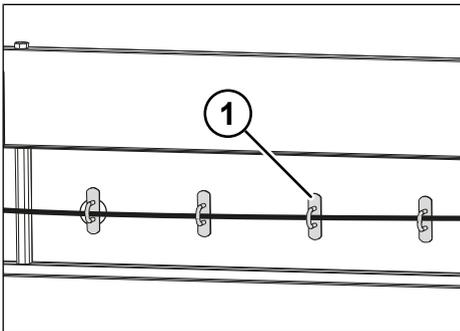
Pattes de fixation de bâche sur la paroi arrière
